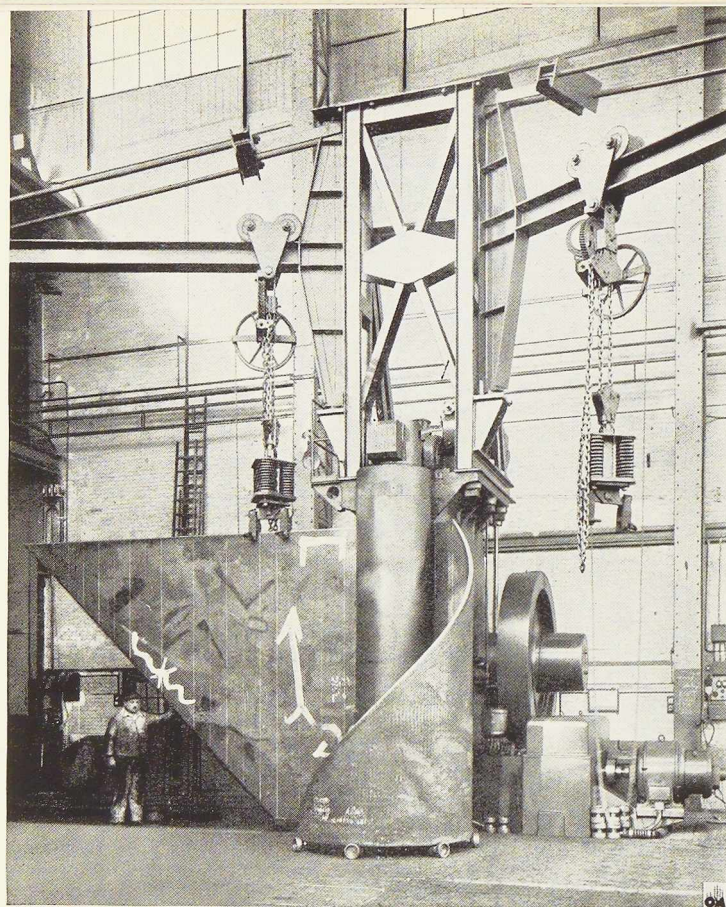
Construction d'un élément de la conduite par assemblage des tôles en forme de parallélogramme, les joints sont disposés suivant une ligne hélicoïdale.
